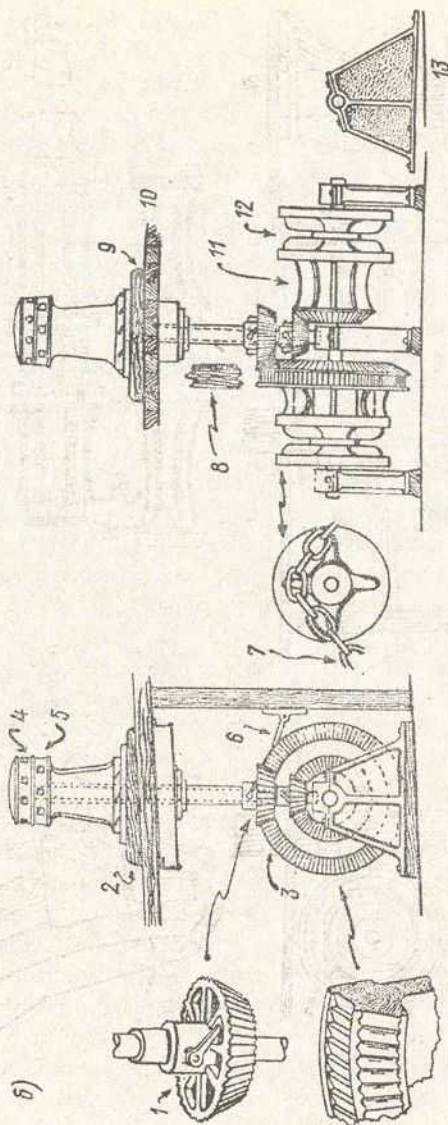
Ручной брашпиль и патент ованый брашпиль с приводом от шпиль а - ручной брашпиль с гандшп у м; 1 - п а м; 2 - 20 - тяговые колеса; 3, 14 - деревянные станины брашпиля; 4, 12 - центральные брашпильные бигени; 5 - подшипник коромысла; 6 - вариант размешения подшипника на осевой стороне; 7 - 1 или 2 стопорных пала; 8, 22 - ползуны однозвуха з жата тягового колеса; 9 - железный шпиндель; 10 - железные вельсы; 11 - тяга рычага; 13 - восьмигранный деревянный балер; 15 - в а гандшпуга в плане; 16 - съемные га ншпуги; 17 - медные оковки; 18 - д еревянная или железная кинша; 19 - б оковые станины; 21 - пал или собачка; 23 - железные вельсы; 24 - шесть железных вельсов; 25 - ж еззные или деревянные турачи м; 6 - п азованный брашпиль; 1 - приводные палы; 2, 9 - лещальные дубовые полушки; 3 - коническая шестерня; 4 - вращение шпиль против часовой стрелки; 5 - вращение шпиль по часовой стрелке; 6 - стопорный пал; 7 - цепь, идущая к роульсу на палубе; 8 - с т а пала; 10 - палуба бака; 11 - турачка; 12 - звезд ожа; В - боковые станины.
